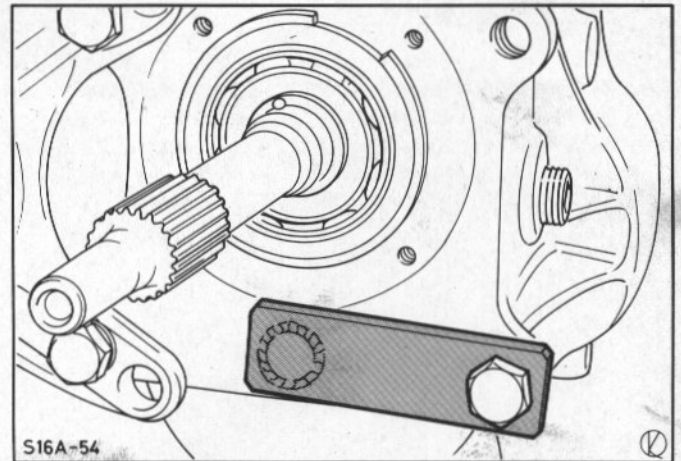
Spezialwerkzeug an Schwungradseite fest-schrauben
